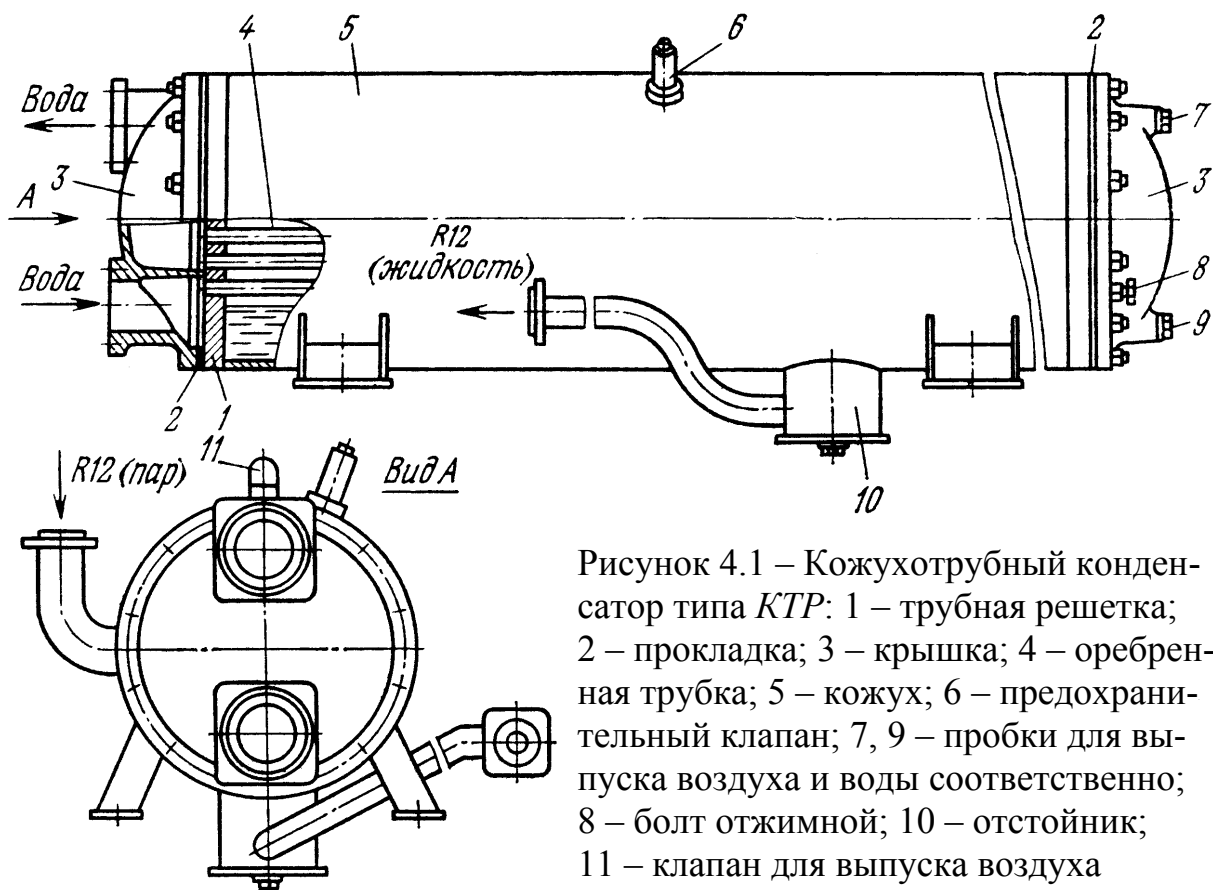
Кожухотрубный конденсатор типа *KTP*: 1 – трубная решетка; 2 – прокладка; 3 – крышка; 4 – оребренная трубка; 5 – кожух; 6 – предохранительный клапан; 7, 9 – пробки для выпуска воздуха и воды соответственно; 8 – болт отжимной; 10 – отстойник; 11 – клапан для выпуска воздуха
